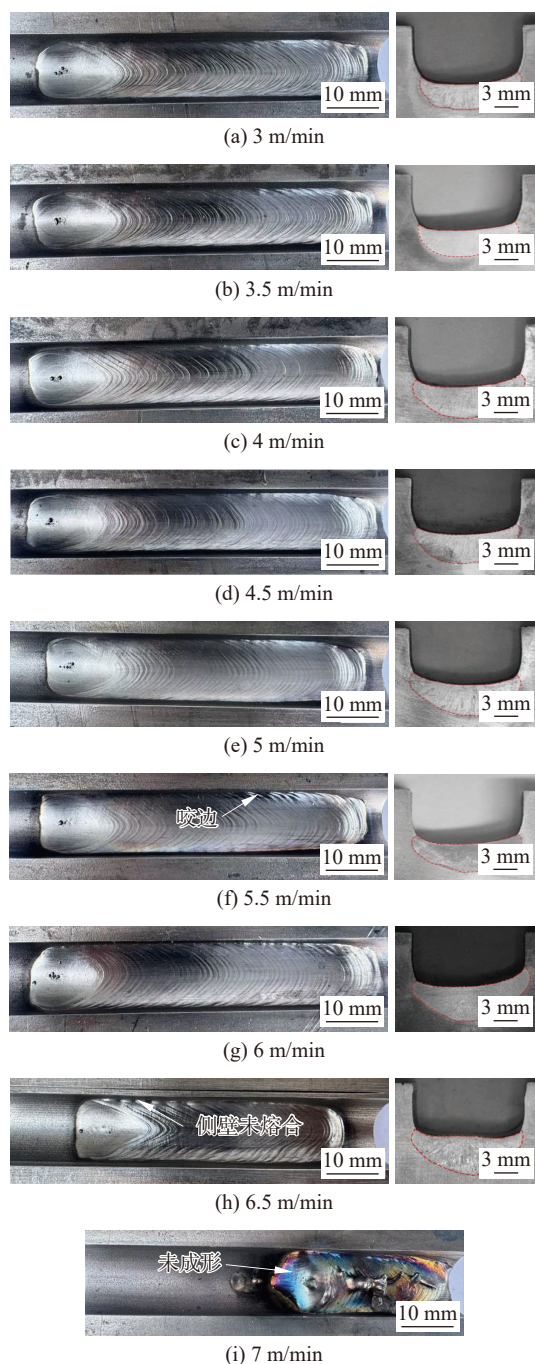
不同送丝速度下焊缝表面成形及截面形貌
